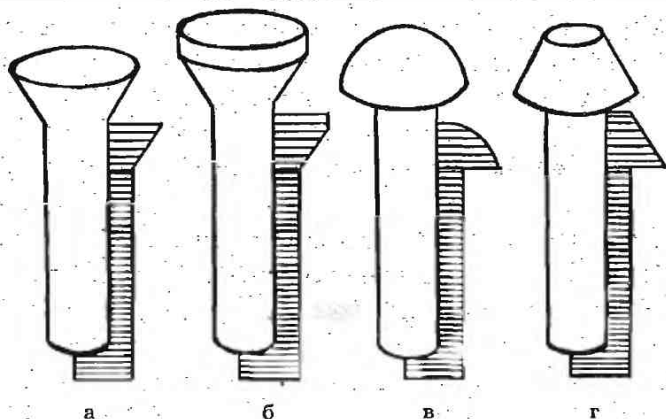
Виды заклепок: а — заклепка с потайной; б — с полупотайной; в — с полукруглой; г — с конической
